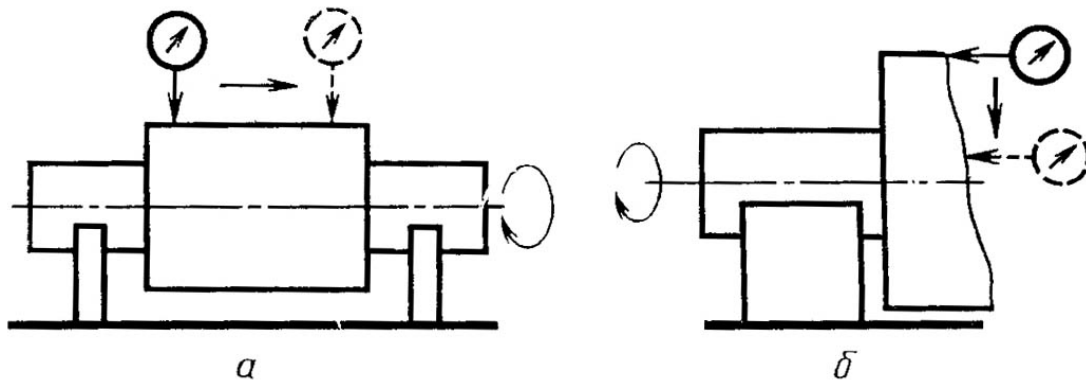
Схема установки контролирующего прибора и движений детали при контроле:
